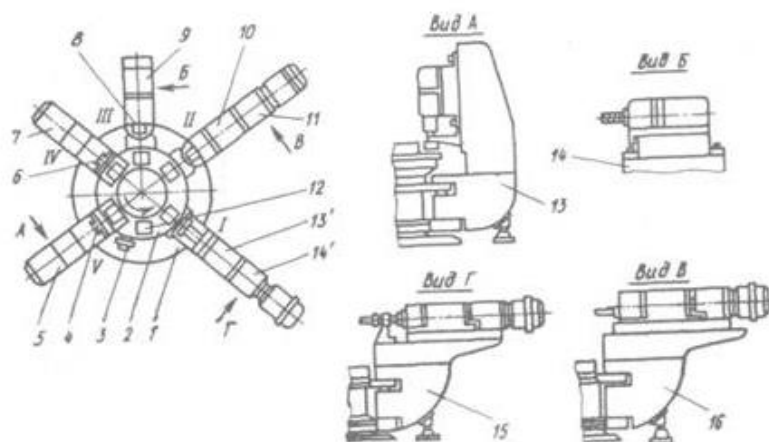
Типовая схема компоновки агрегатного станка для обработки кронштейна
